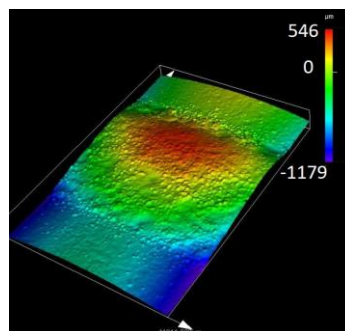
Vzorek CE5\_03; zobrazení povrchu návaru
